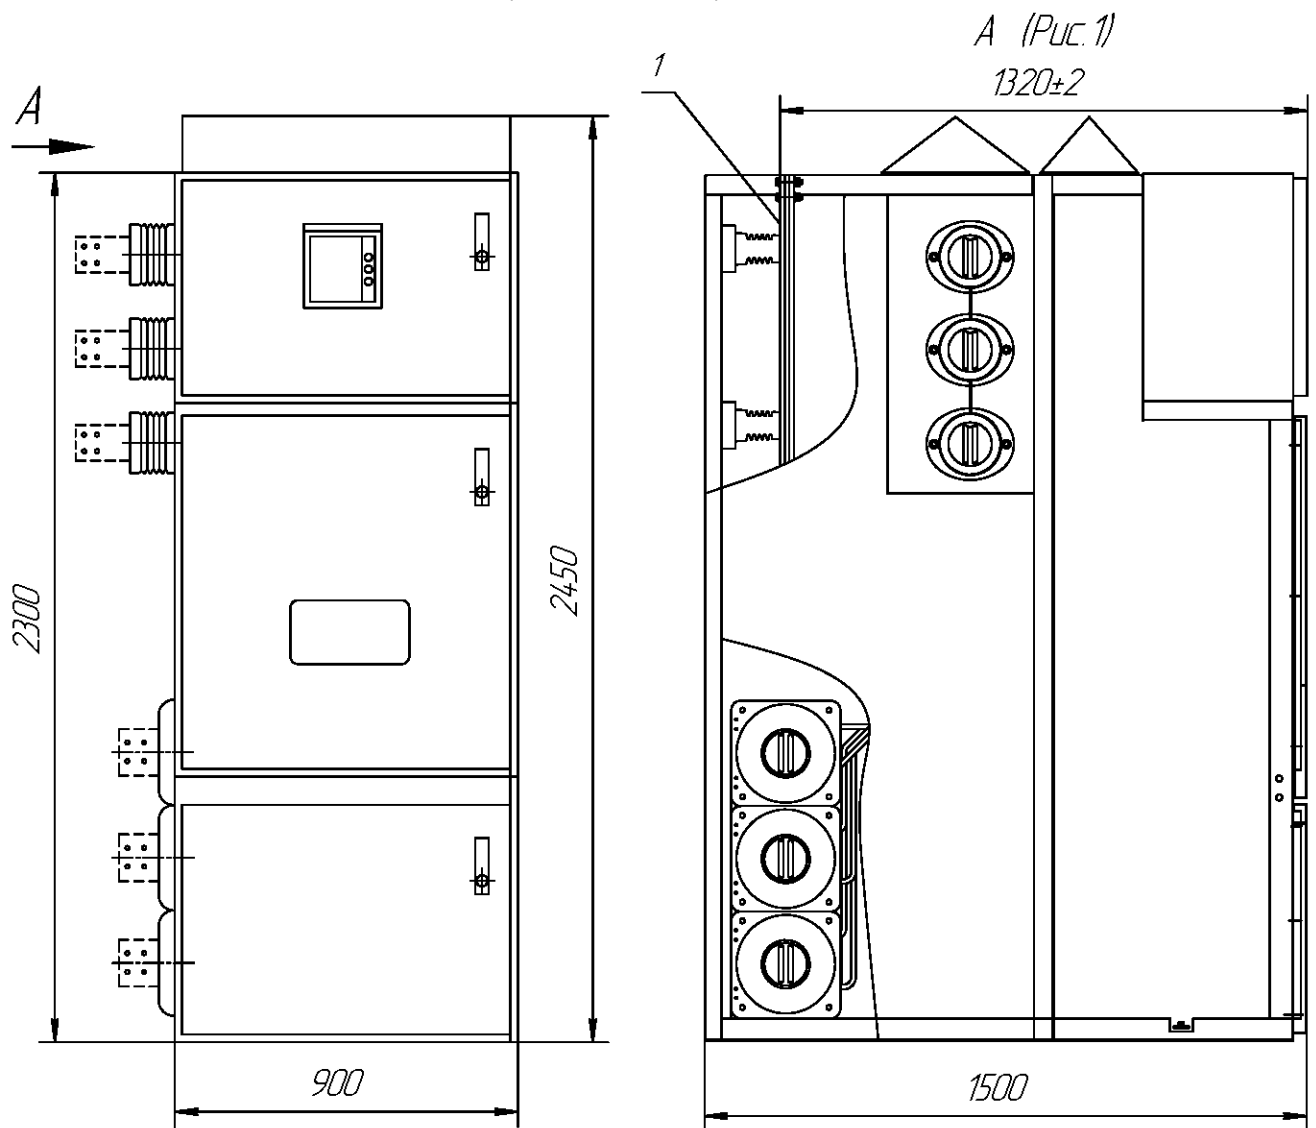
Габаритные, установочные, присоединительные размеры шкафов Шкаф типа ШВВ на номинальные токи 2000..4000 А с воздушным вводом и линейными шинами
